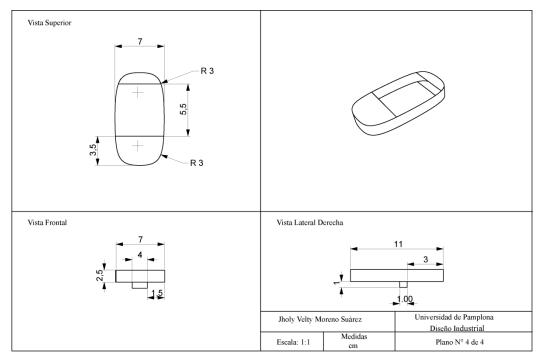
Plano 4 Contenedor. Fuente: Autor
